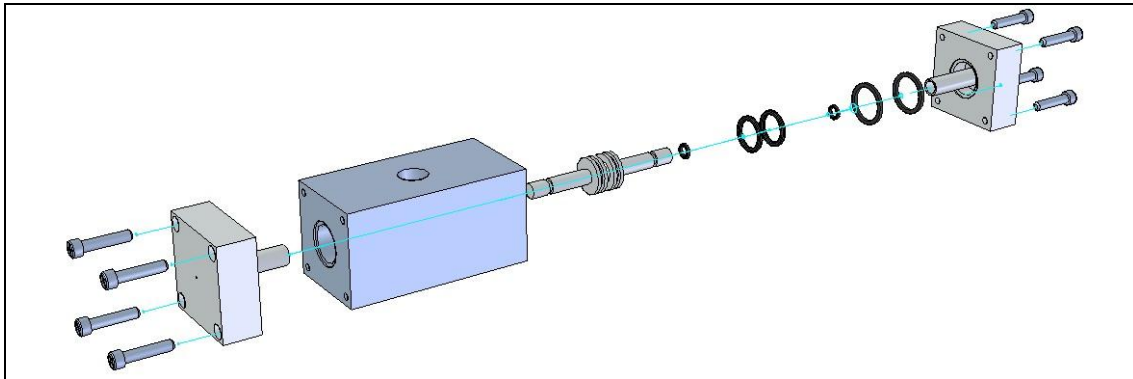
41 - Modelo de Válvula selectora – Explosionado
